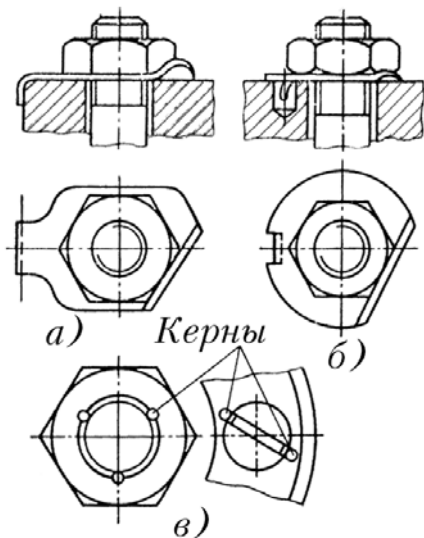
Стопорение гайки шайбой с наружными выступами (а) и (б) и с помощью кернера.
